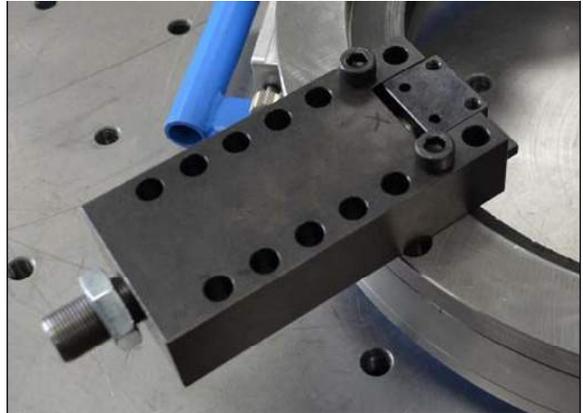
ENSEMBLE DE PIEDS DE SERRAGE FIXÉ À LA RDU (FF1200 ILLUSTRÉE)
